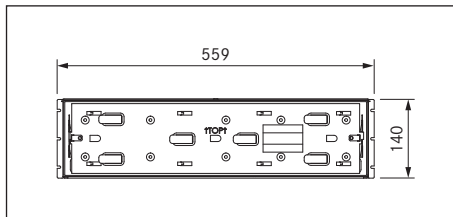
Dimensões do aparelho MS140, vista frontal
